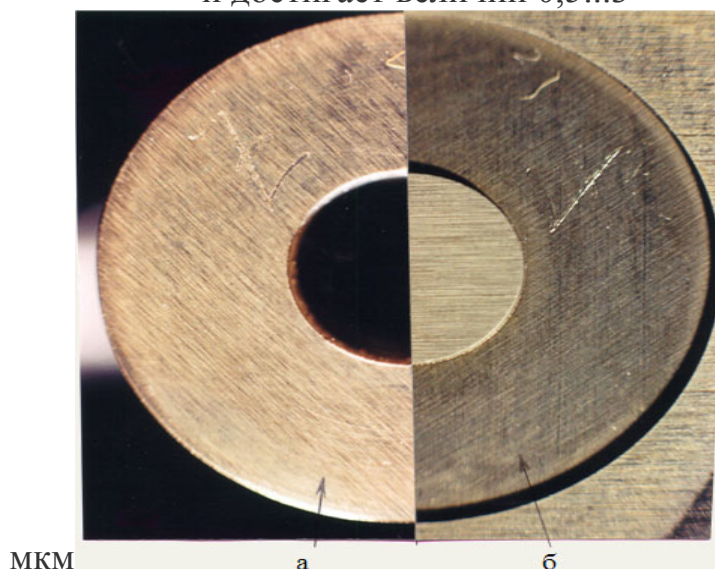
Общий вид торцевой поверхности электрода-инструмента из латуни с регулярными линиями микровыступов (Ra 0,8...1,25), оставленных шлифовальным кругом (а) и общий вид обработанной поверхности детали (б) из закаленной хромистой стали, на которой после обработки скопировался микропрофиль торца электрода-инструмента
